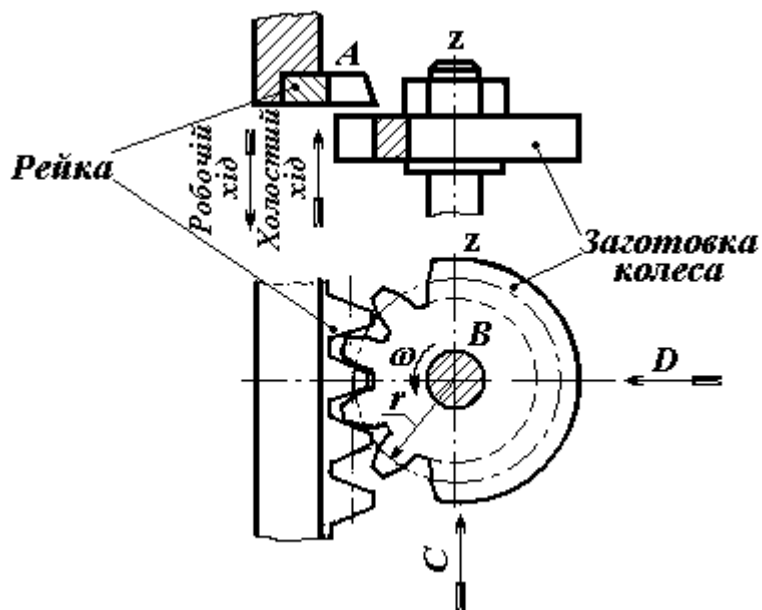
Схема нарізування зубчастих коліс методом обкатки
